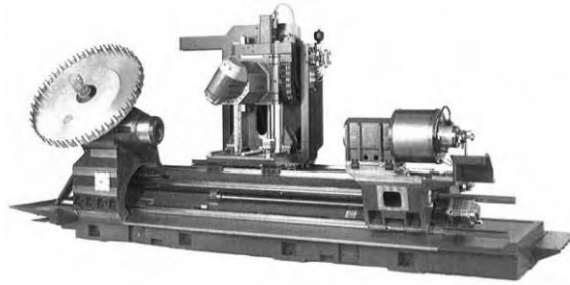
Верстат СТХ, оснащений токарно-фрезерним шпинделем фірми DMG
